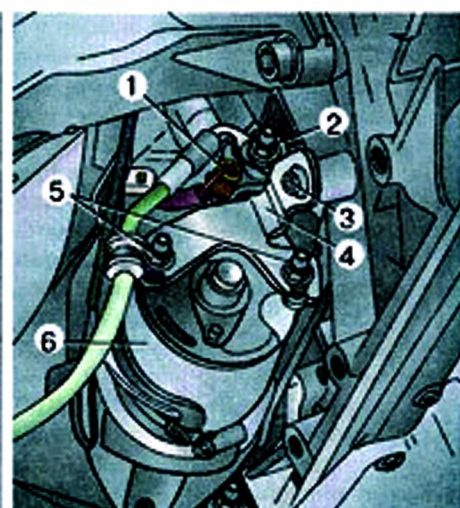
Крепление стартера на двигателе автомобиля Audi 80/90: 1 – вывод «50»; 2 – вывод «30»; 3 – болт крепления кронштейна стартера; 4 – кронштейн крепления стартера; 5 – гайки крепления стартера к кронштейну; 6 – стартер
